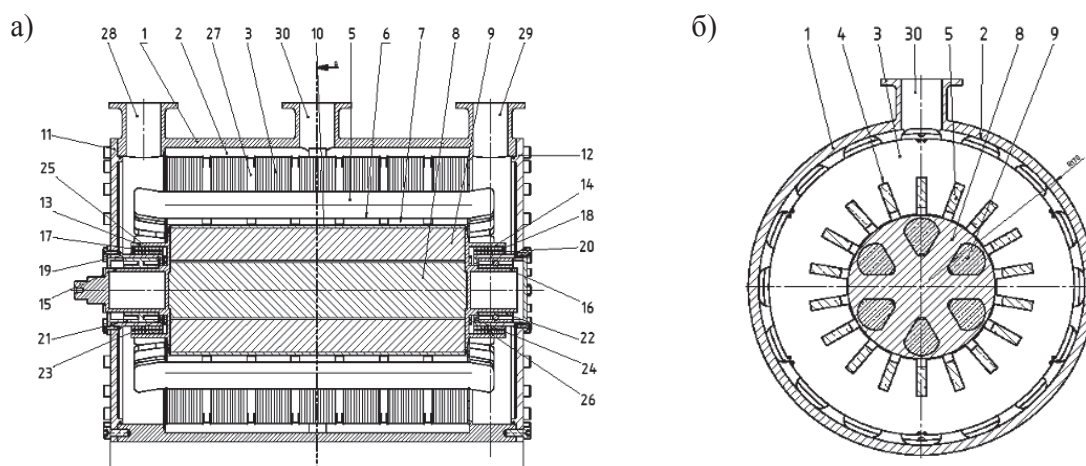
Продольный (а) и поперечный (б) разрезы генератора: 1 – корпус генератора; 2 – продольные вентиляционные каналы; 3 – пакеты сердечника статора; 4 – пазы; 5 – катушки обмотки статора; 6 – пазовый клин; 7 – пазовые вентиляционные каналы; 8 – вал; 9 – постоянные магниты индуктора с радиальным намагничиванием; 10 – бандаж ротора; 11, 12 – торцевые щиты генератора; 13, 14 – цапфы ротора со стаканами и 15, 16 – центральными выступами; 17, 18 – наружные и 19, 20 – внутренние кольца постоянных магнитов радиальных магнитных подшипников; 21, 22 – страховочные шарикоподшипники; 23, 24 – наружные и 25, 26 – внутренние кольца упорных магнитных подшипников; 27 – радиальные вентиляционные каналы; 28, 29 – патрубки подачи охлаждённого газа; 30 – патрубков вытяжки нагретого газа из кольцевого канала генератора
